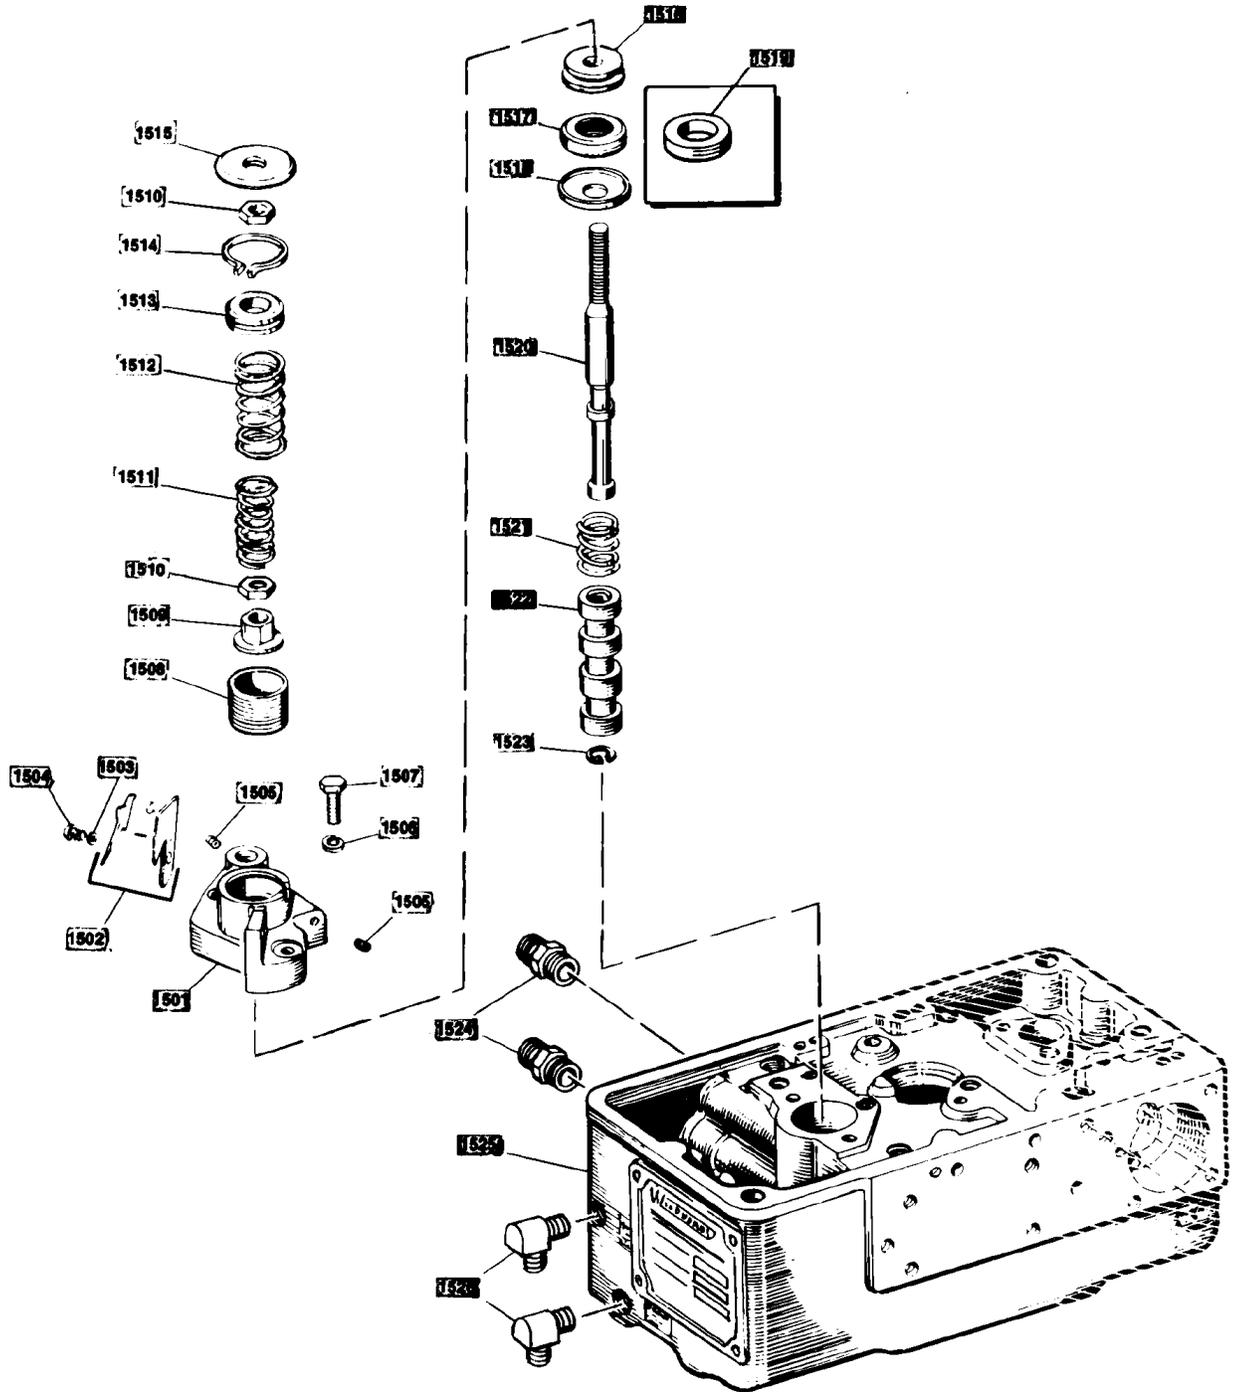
Vista Detalhada da Válvula Piloto de Controlo de Carga
